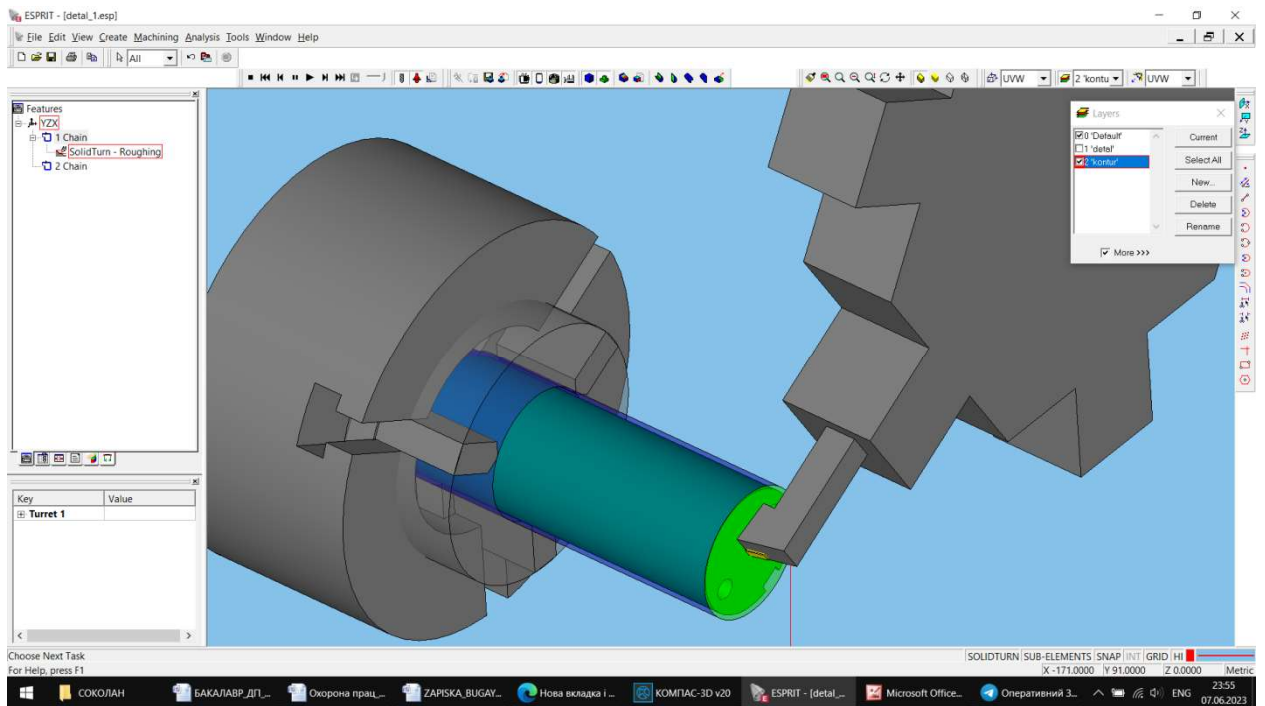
Траєкторія руху металорізального інструменту при обробленні контуру деталі «палець»
